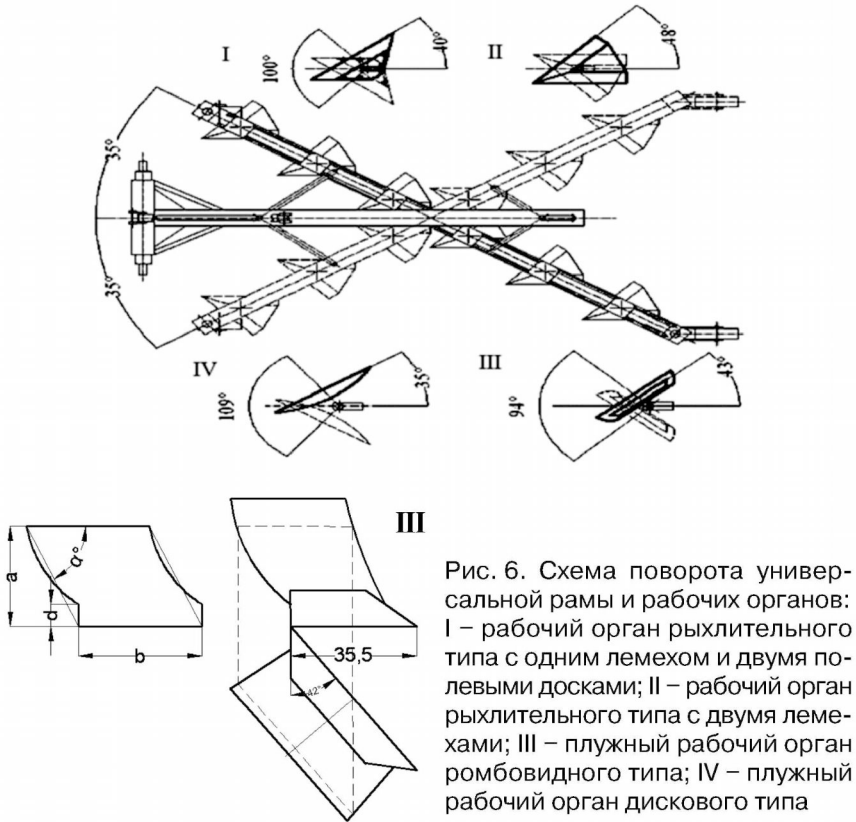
Схема поворота универсальной рамы и рабочих органов: I – рабочий орган рыхлительного типа с одним лемехом и двумя полевыми досками; II – рабочий орган рыхлительного типа с двумя лемехами; III – плужный рабочий орган ромбовидного типа; IV – плужный рабочий орган дискового типа
